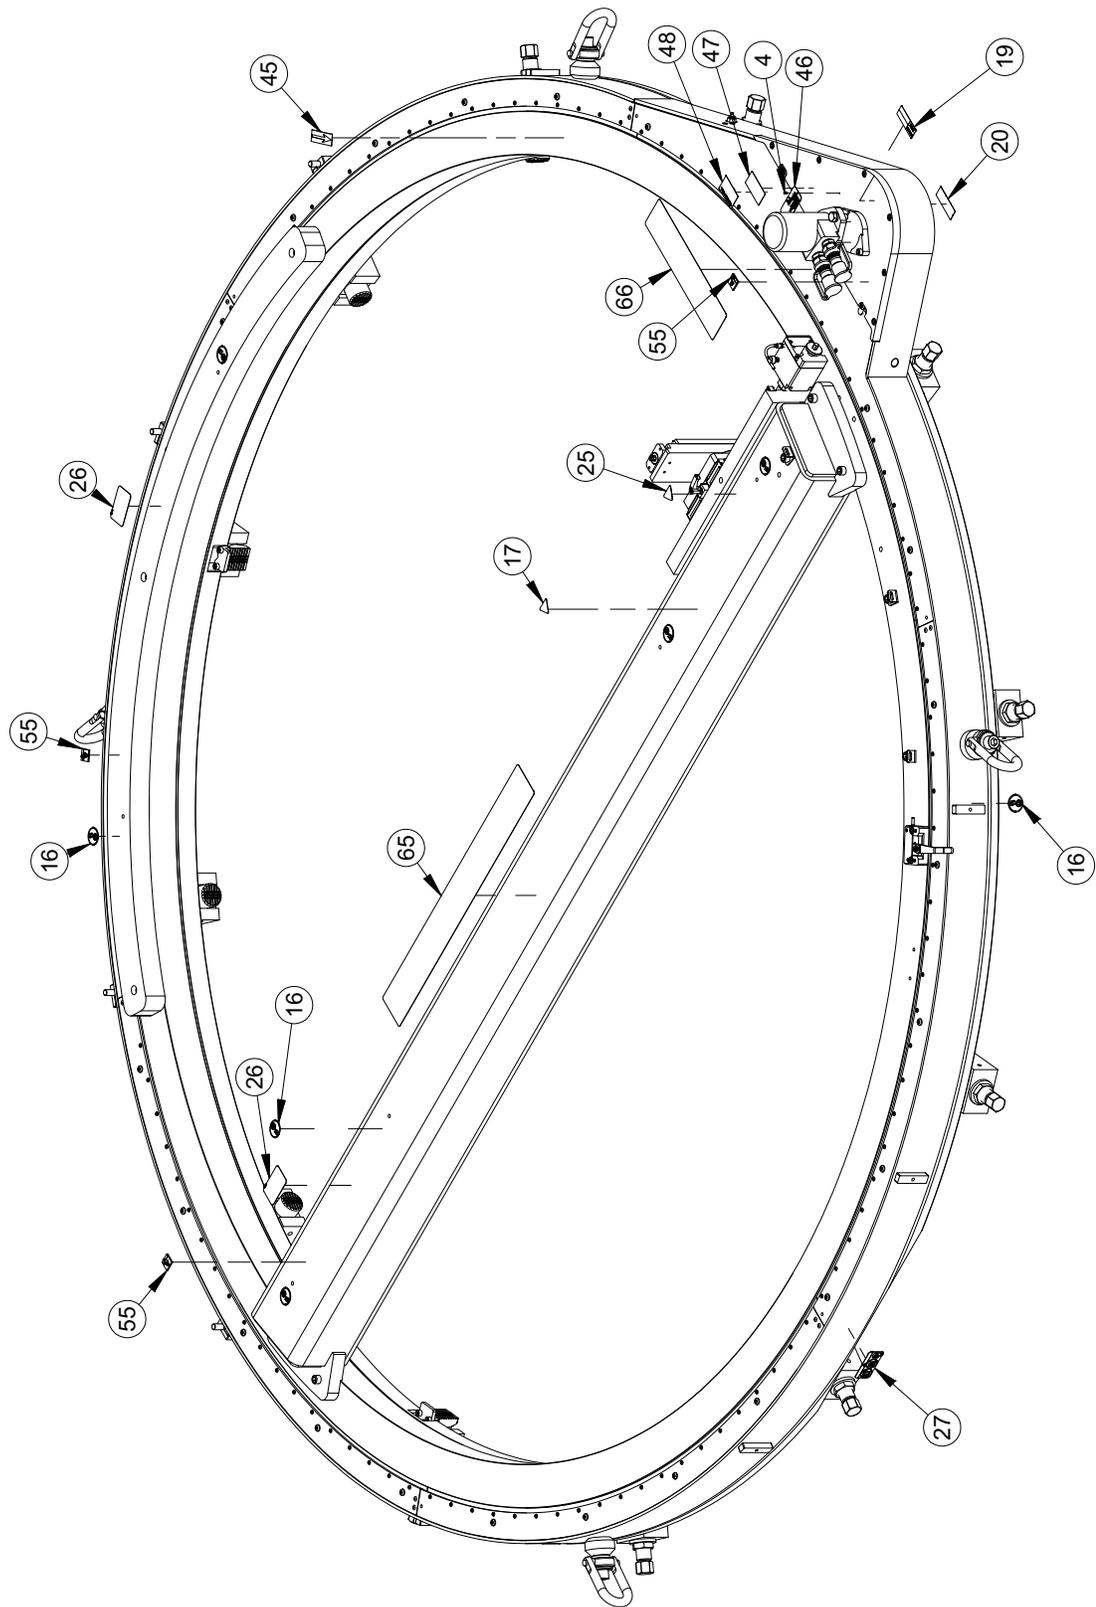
ODF110 SPEED FACER EMBLEMES DES ÉTIQUETTES (RÉF. 7639-S2)
